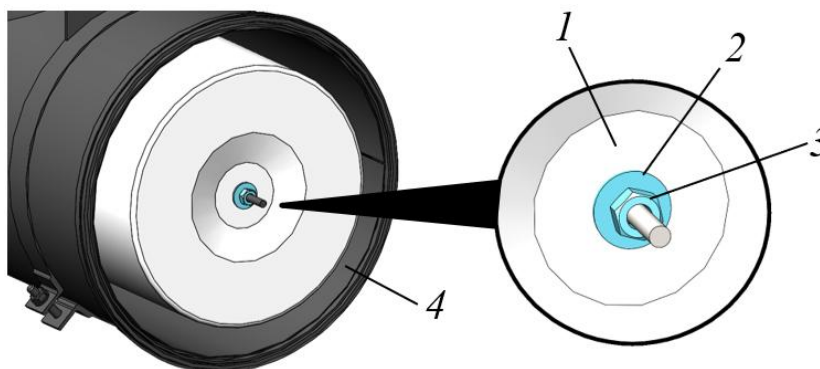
Извлечение основного фильтрующего элемента из корпуса фильтра
